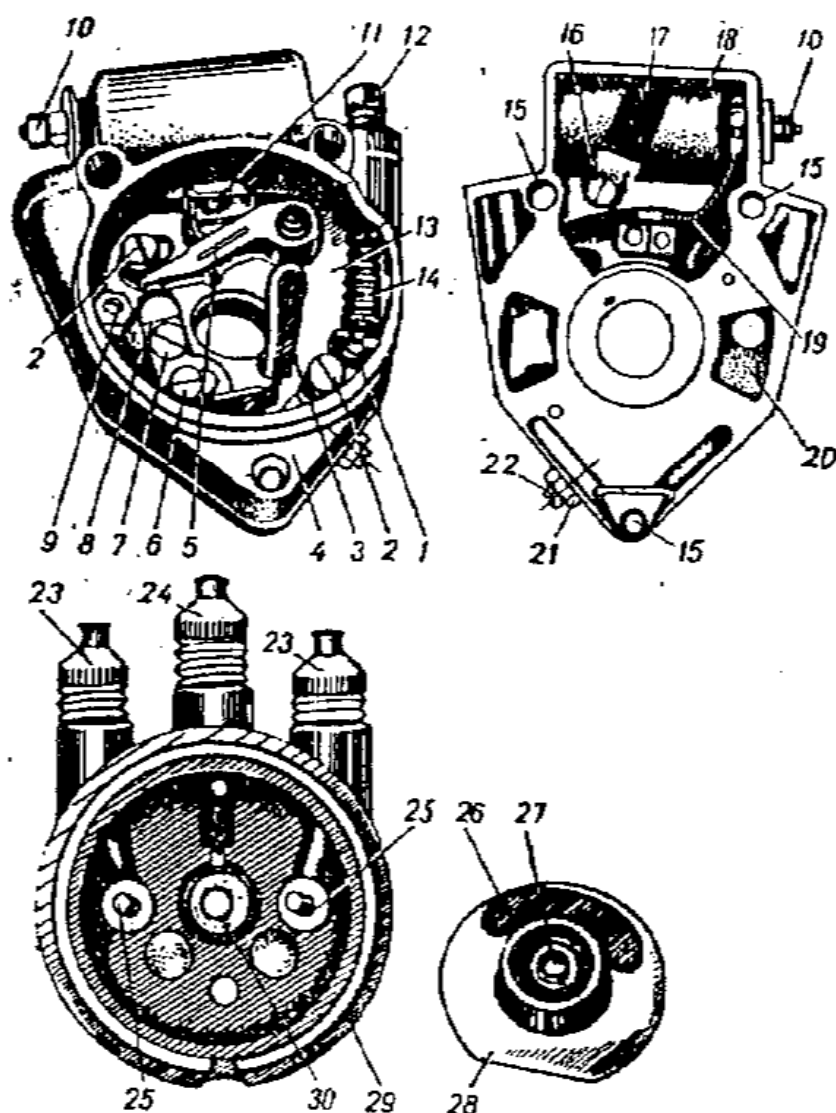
Устройство прерывателя-распределителя ПМ05:
